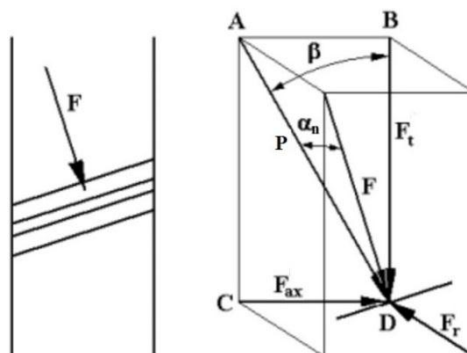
Descomposición de fuerzas en un diente de engranaje.
